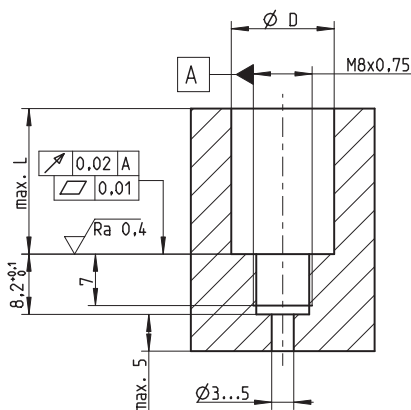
Einbau zurückversetzt. Bohrung ø gemäss Werkzeug, Bild 4 oder Bild 5
